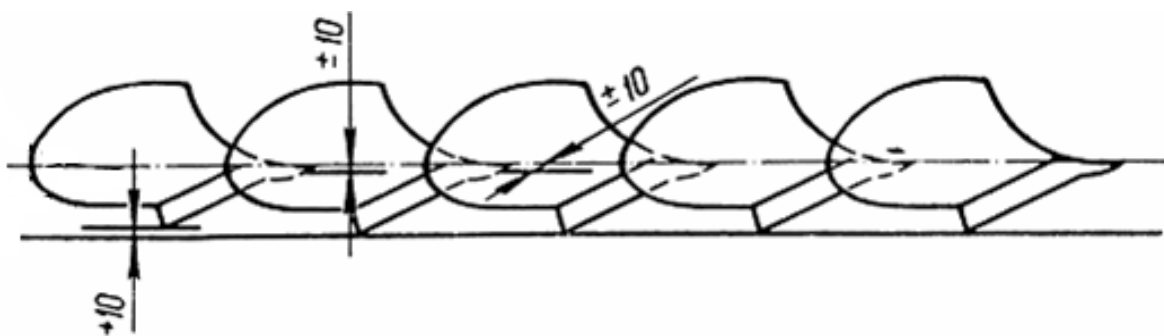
Схема перевірки положення корпусів плуга за допомогою шнура
